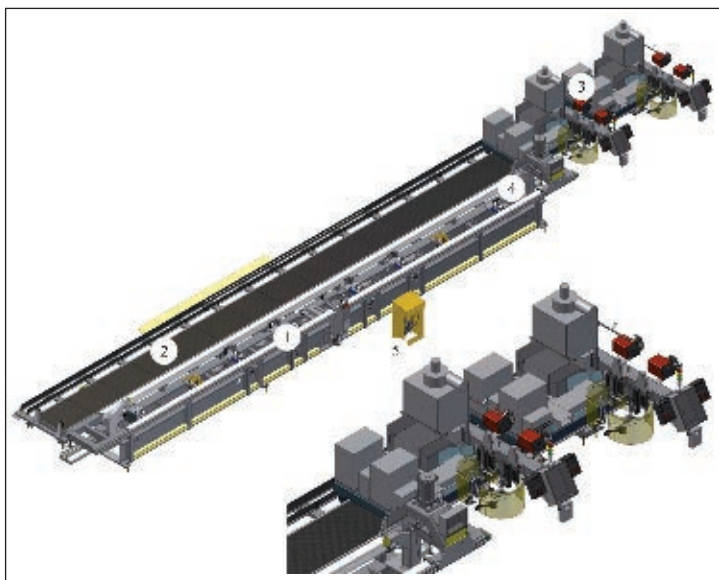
Установка для автоматической сварки хребтовой балки с двутавром: 1 — станд; 2 — транспортная система; 3 — тележки для перемещения сварочных автоматов и источников питания; 4 — тележка для установки двутавра; 5 — пульт управления
